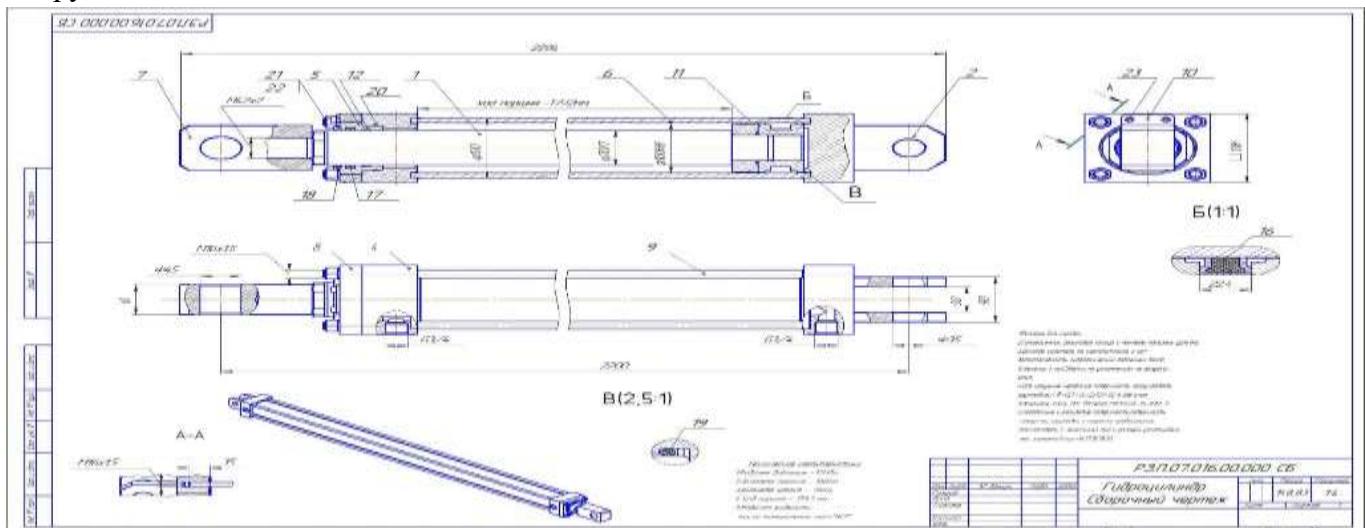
Конструкции гидроцилиндров промышленного оборудования
